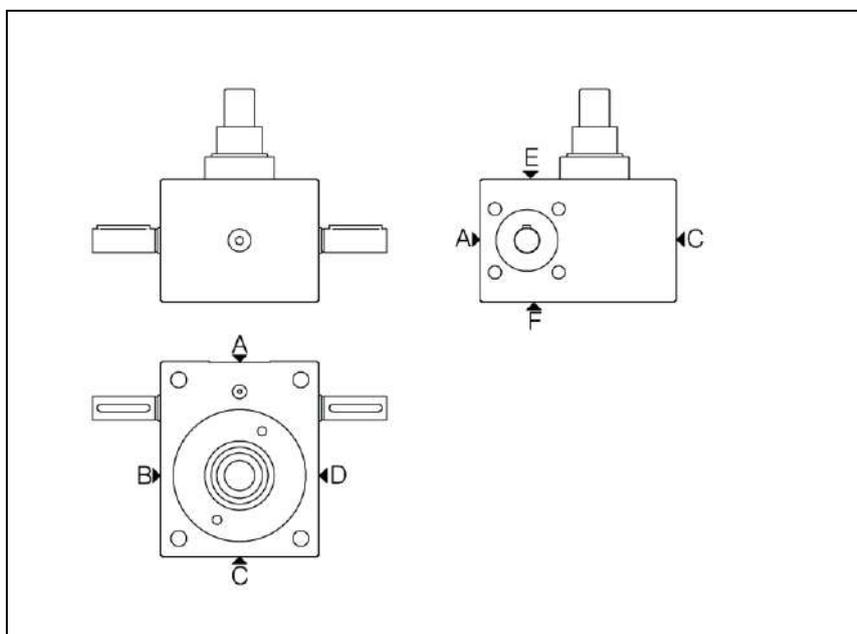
Vue d'ensemble vérin de levage ZIMM
